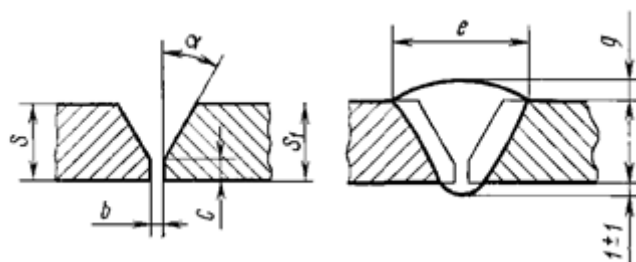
Эскиз сварного соединения С17 ГОСТ 14771-76
